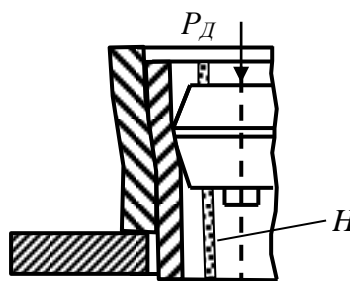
Схема несвободного дорнования отверстий трубчатых заготовок (H – сварной шов)
